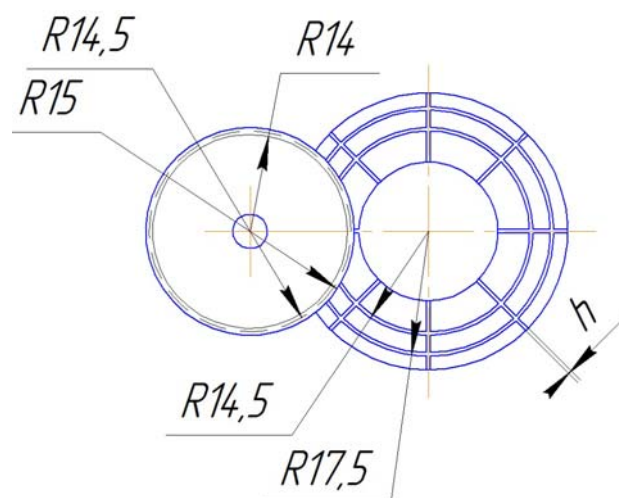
Схема обработки плоской поверхности детали и полировального инструмента
